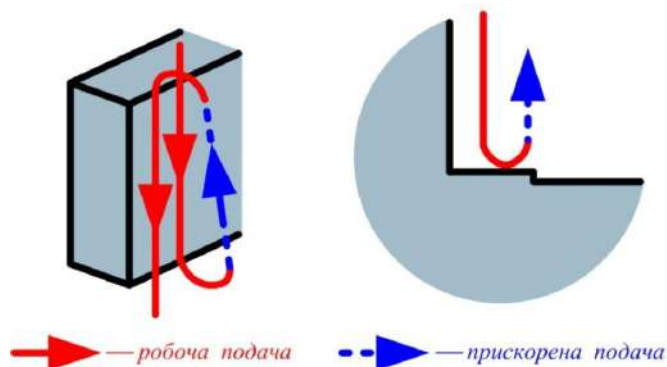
Відведення плунжерної фрези для запобігання повторного різання
